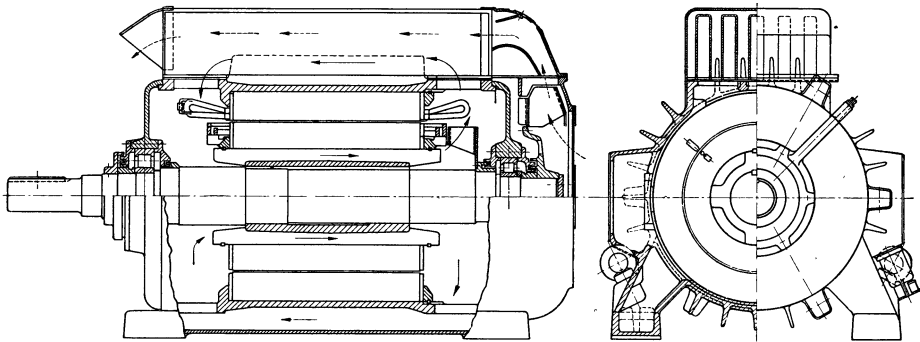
Gekapselter Motor mit Außenbelüftung und Oberflächenkühler (AEG.).
